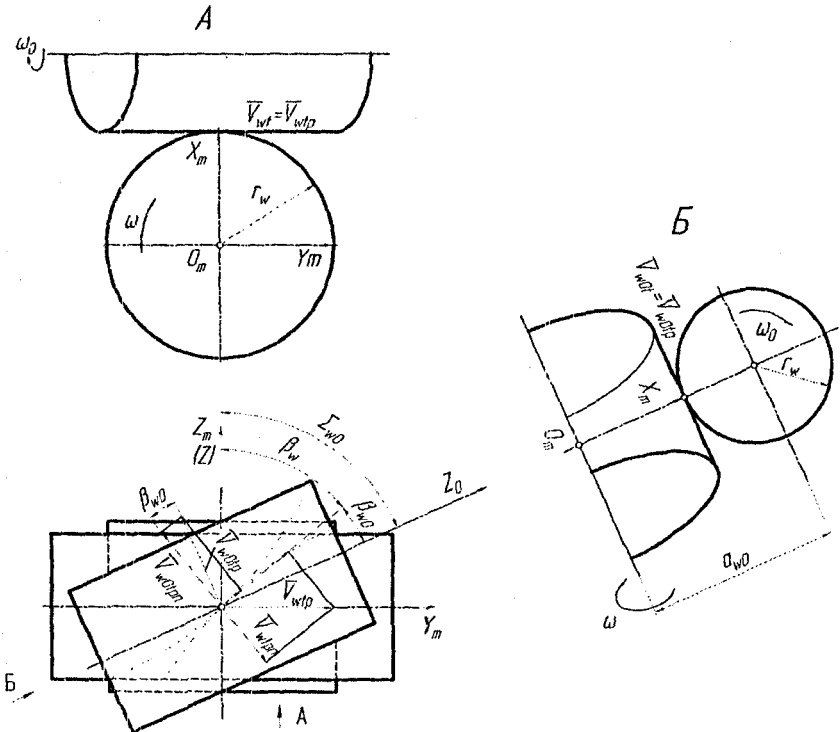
Схема расположения начальных поверхностей винтовой пары и векторов скоростей при условно положительном направлении вращения
